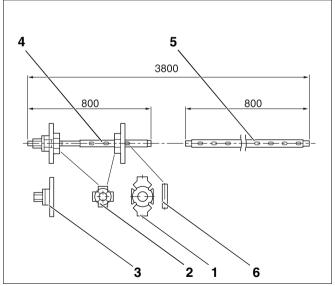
Kesselpresswerkzeug Größe 2.3 (Maße in mm)
